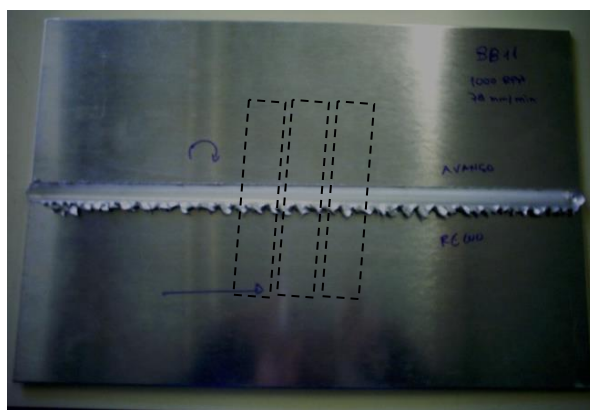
Provette obtido após a soldadura de FSW.
